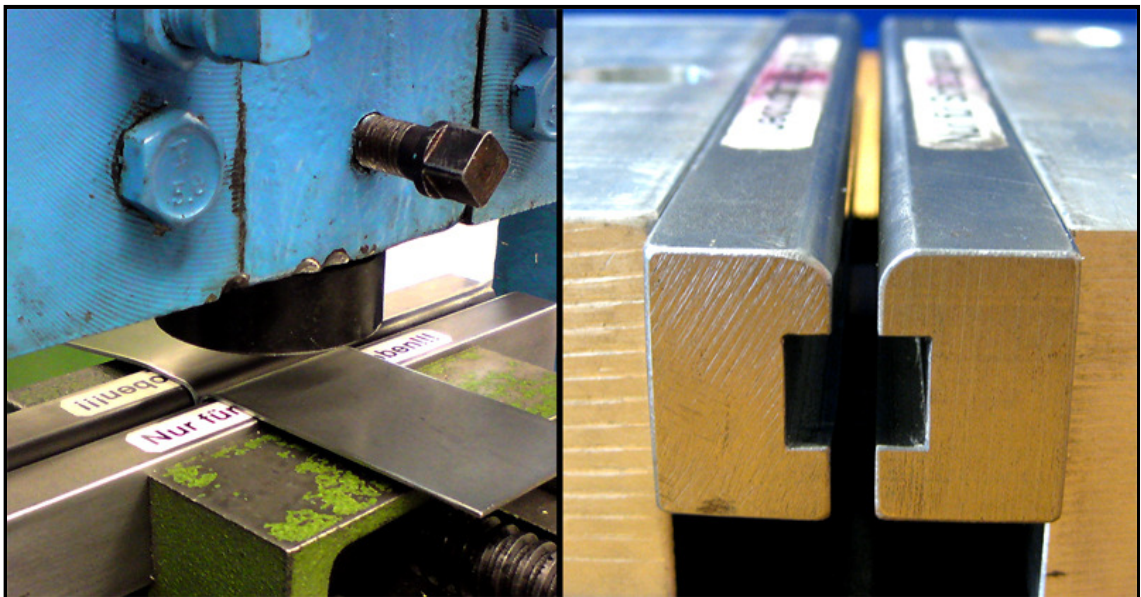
Spannbacken für Schälzugproben; links: in Standard-Schraubstock unter Balance-Presse; rechts: in Spezial-Halterung für dicke Bleche mit hydraulischer Presse
